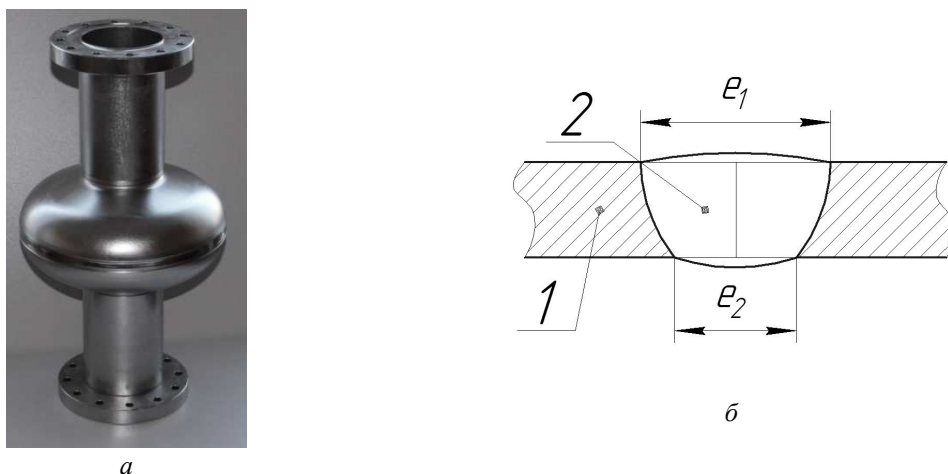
1,3 ГГц одноклеточный СВЧ ниобиевый резонатор (а) и изучаемая геометрия сварного шва (б); 1 – основной металл; 2 сварной шов
